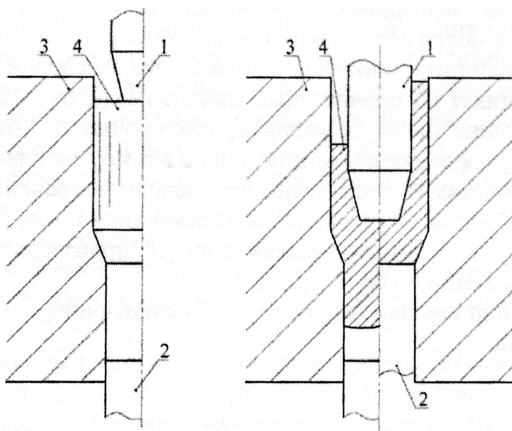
Схема работы инструмента на 2-ой позиции: 1 – пуансон; 2 – контрпуансон/выталкиватель; 3 – матрица; 4 – заготовка
